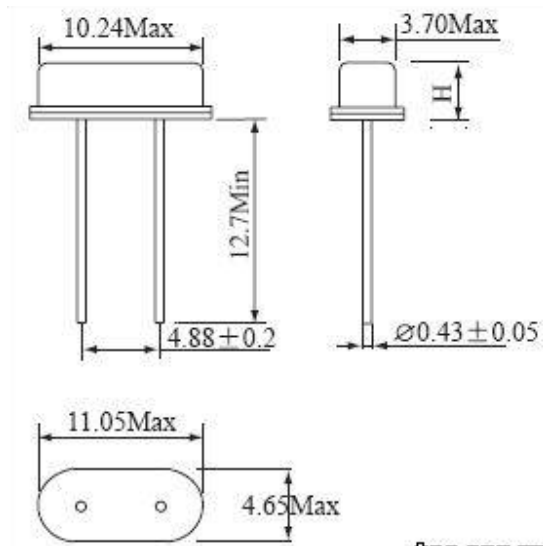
Габаритні розміри кварцевого резонатора HC-49U-16МГц
